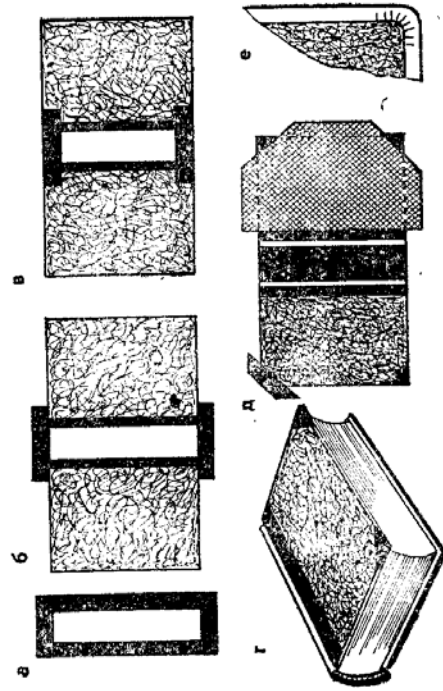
Изготовление составной переплетной крышки: а — наклеивка отстав на корешок; б — прикантовка картонных сторонков; в — подклеивка концов корешка; г — примерка на блок; д — наклеивка уголков; е — заделка закругленного угла
